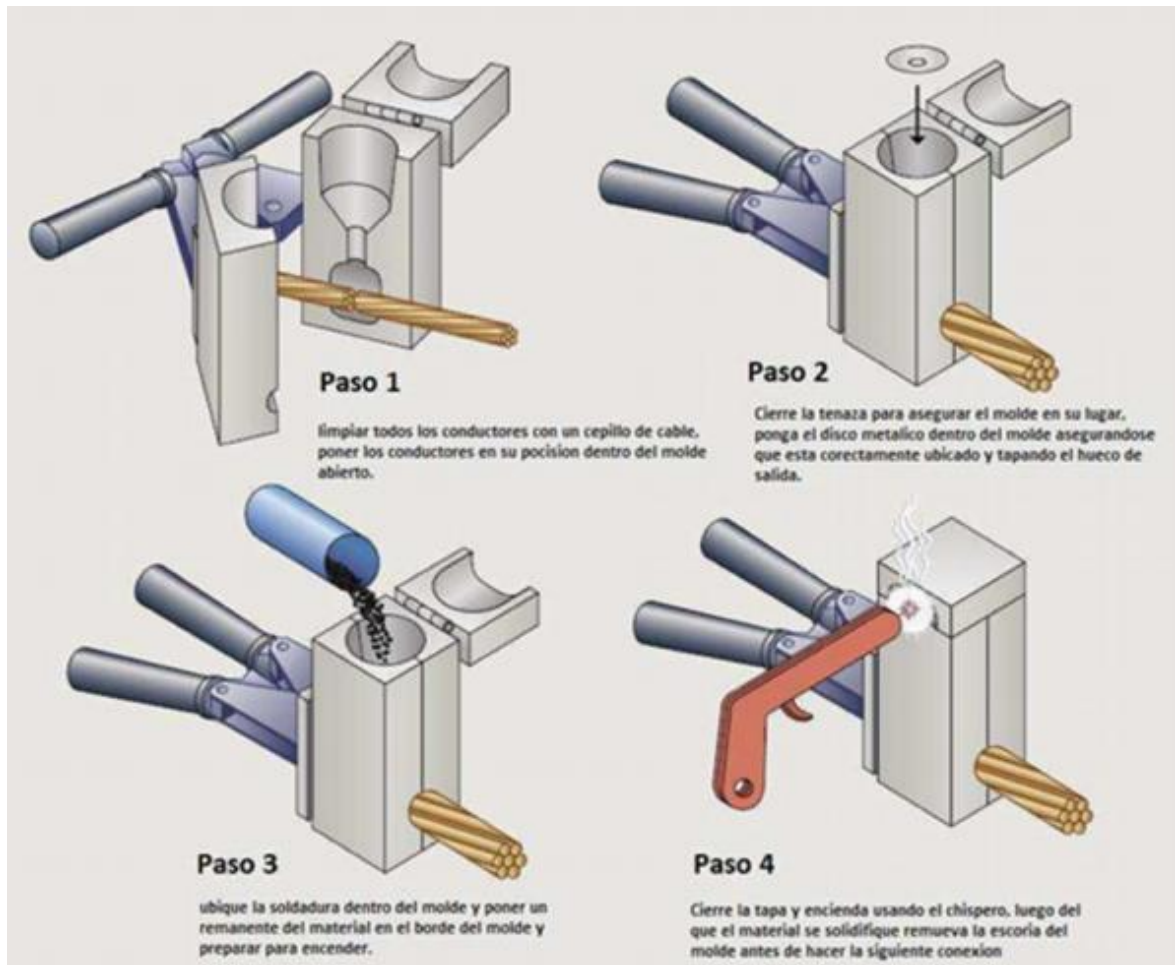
Proceso de conexión por soldadura exotérmica.
